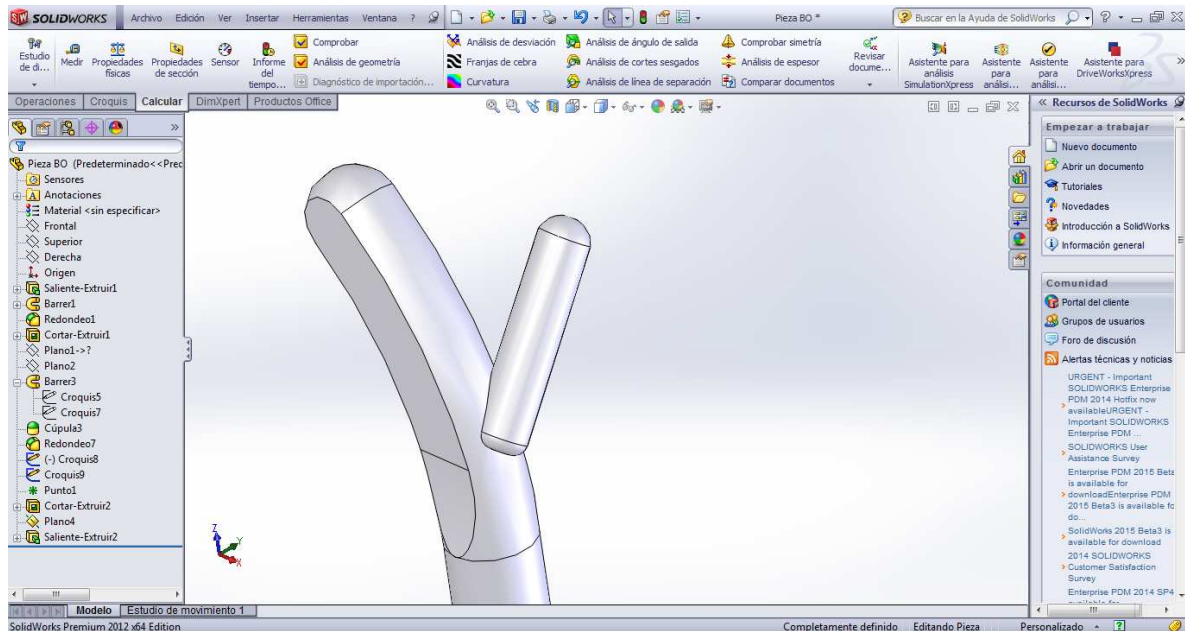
Rediseño de parte metálica con varilla soldada de 4 mm de diámetro
